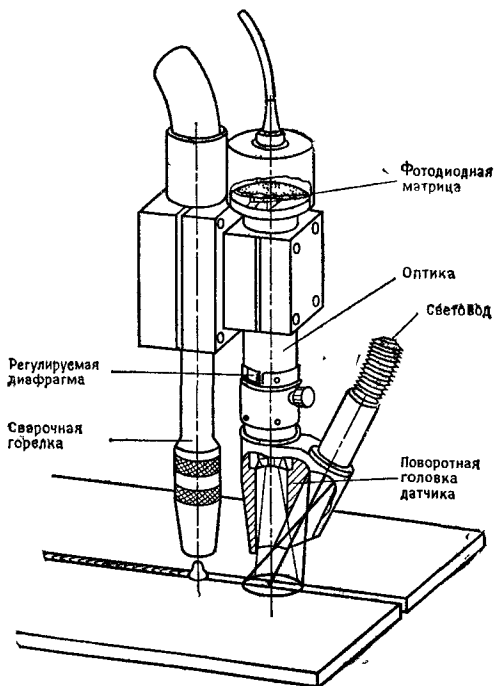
Оптический датчик для управления процессом сварки в среде защитного газа.
